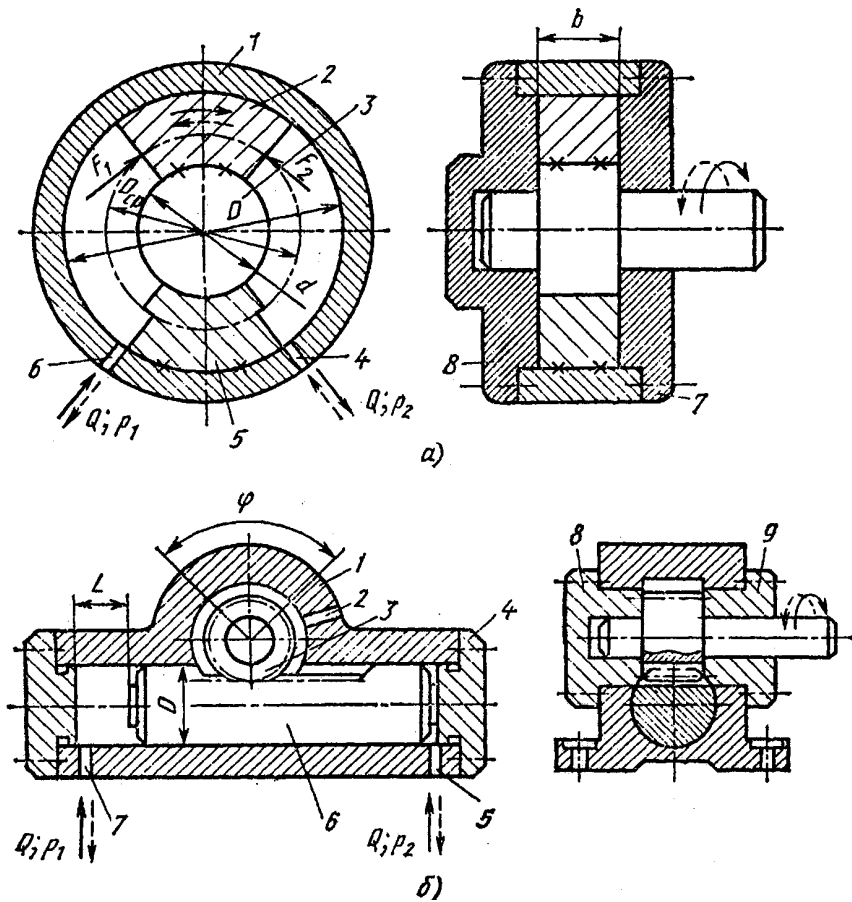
Схема конструкции поворотных гидродвигателей в виде моментного лопастного цилиндра и силового плунжерного цилиндра с реечной передачей
